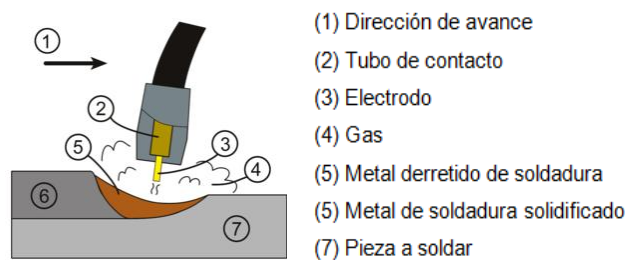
Elementos del proceso de soldadura GMAW
